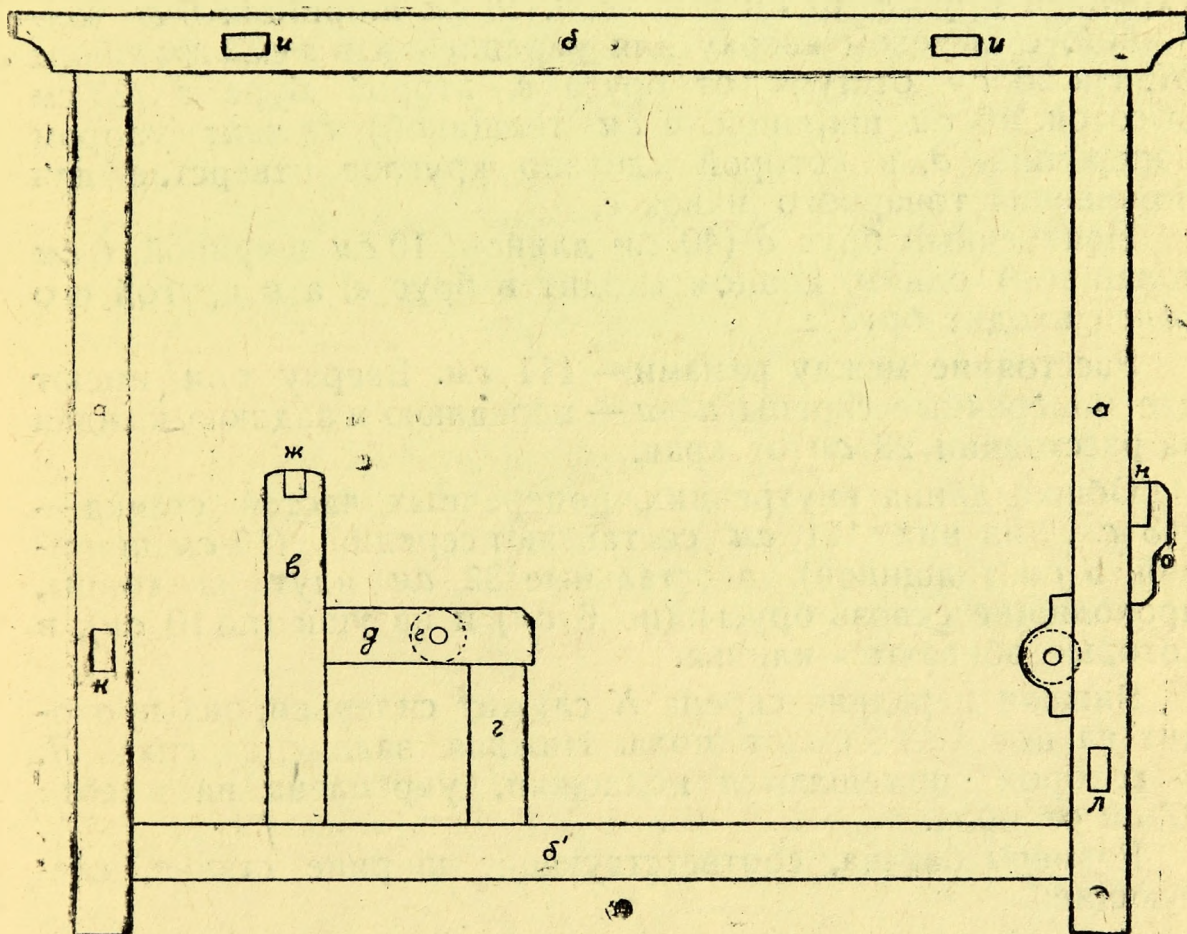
Боковой вид рамы станка для shaftовой машины.
